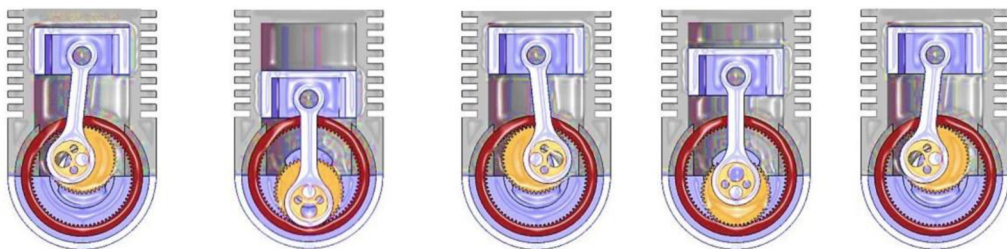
Sací a expanzní zdvih mechanismu EXlink upraveno [6]
